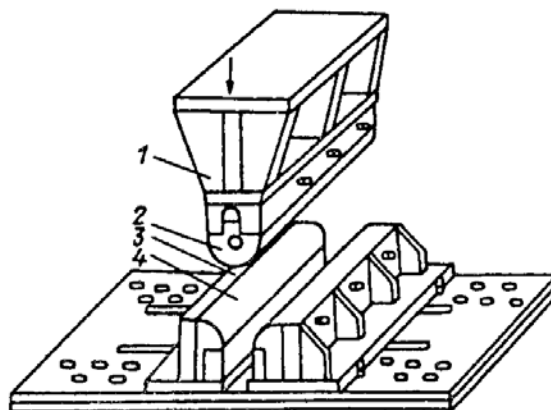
Універсальний штамп для гнуття листових деталей [11]
